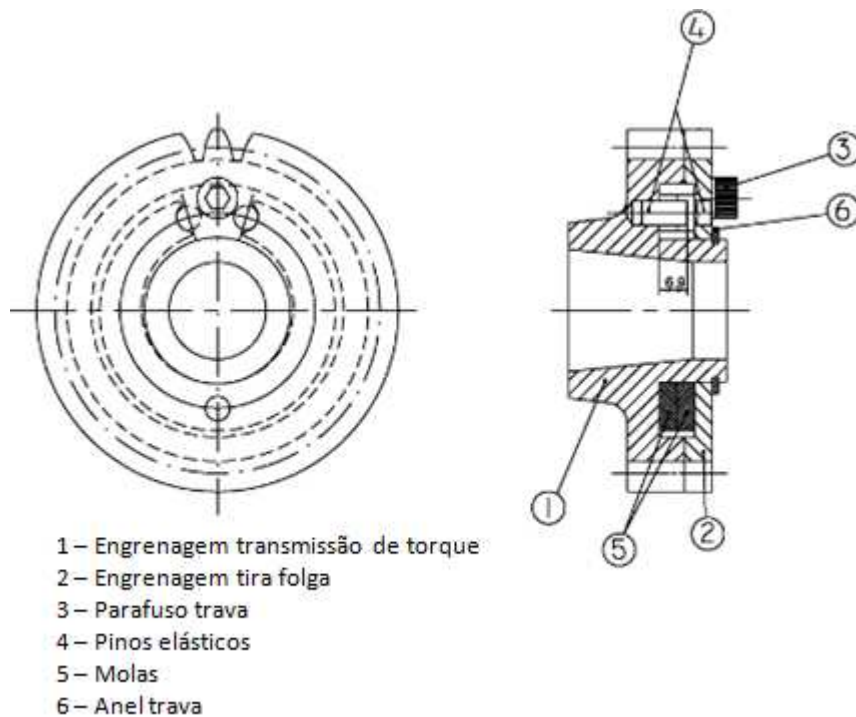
Detalhes da engrenagem pré-tensionada.
